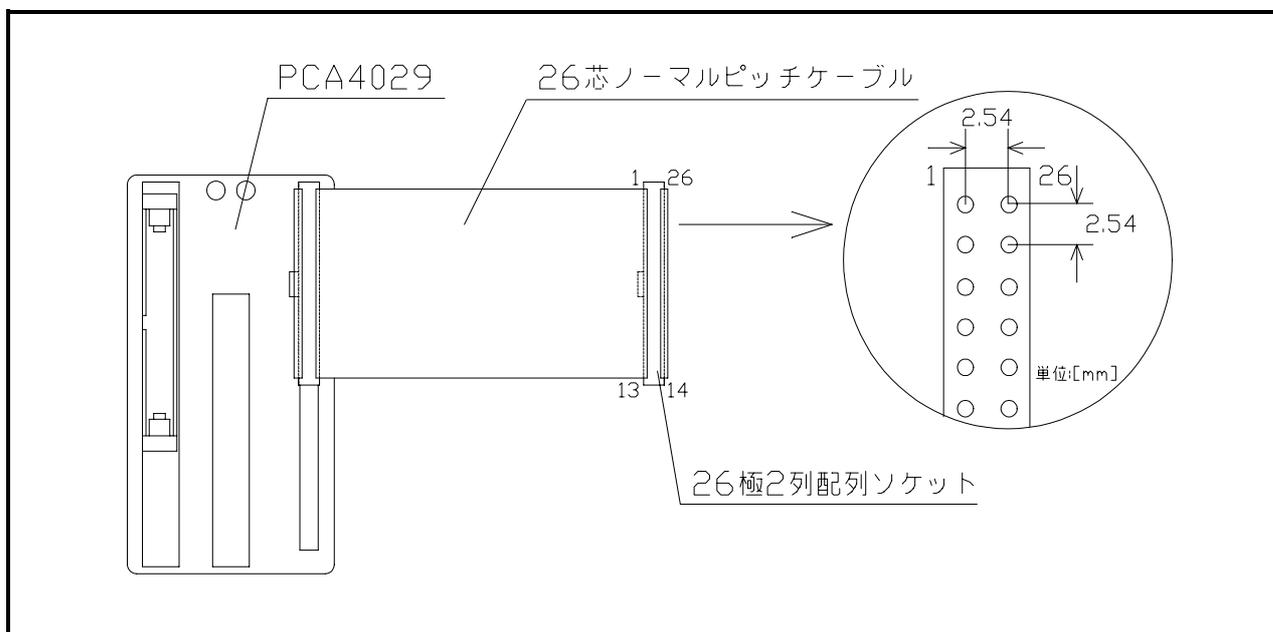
26 芯ノーマルピッチケーブル ピン配置図
